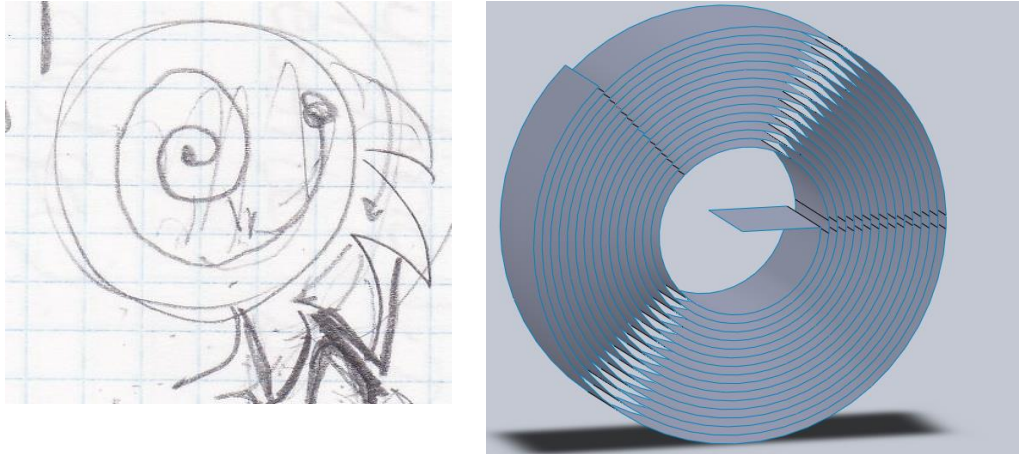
Croquis de la rueda dentada del trinquete con el sistema para almacenar el cable.
